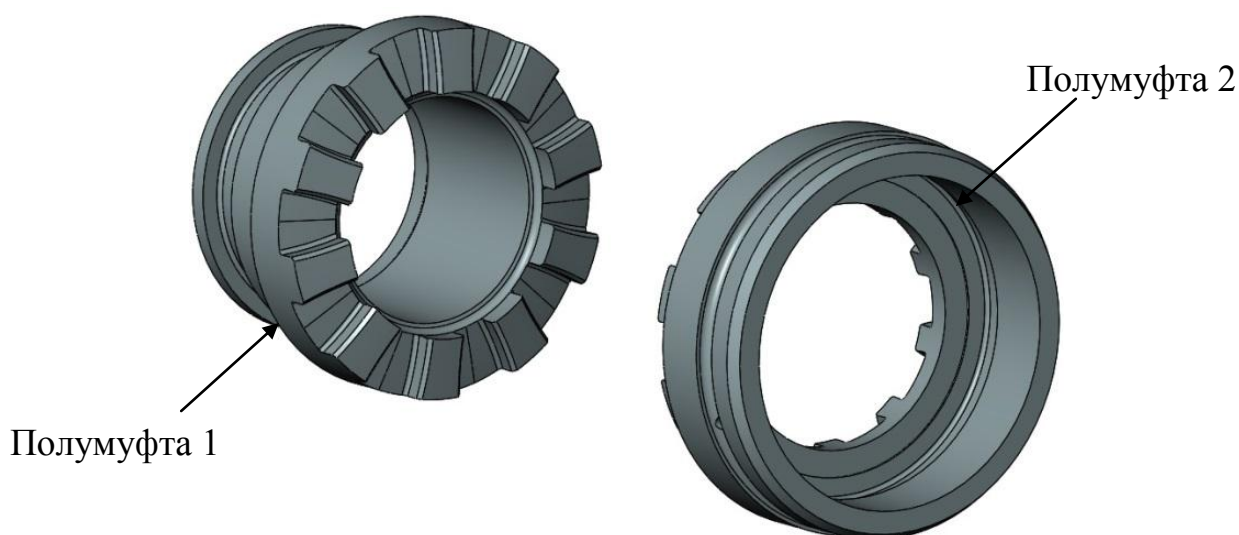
Общий вид муфты блокировки межколесного дифференциала
